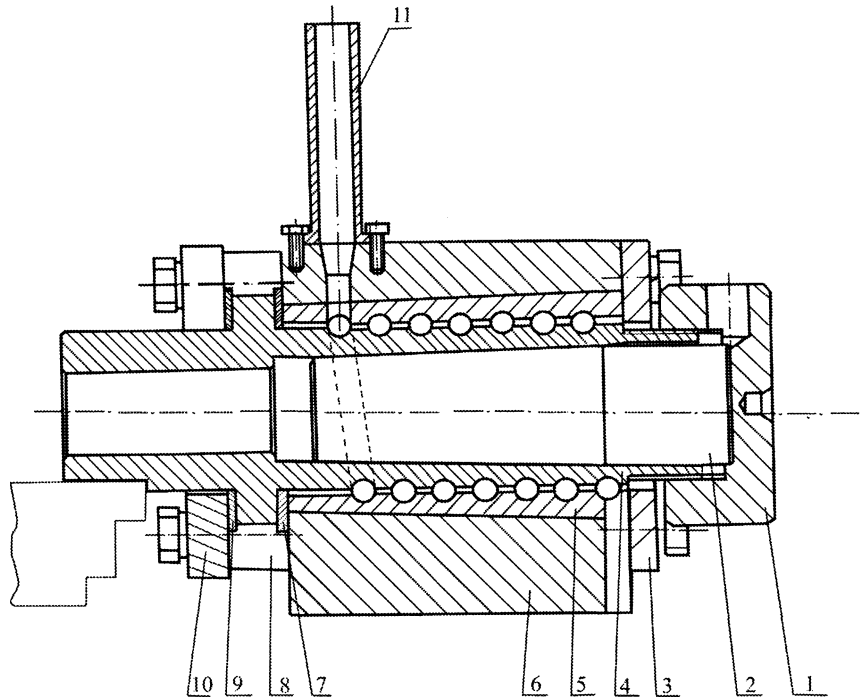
Инструмент для обкатки шариков: 1 – гайка прижимная; 2 – оправка; 3 – крышка; 4 – шнек; 5 – вставка; 6 – корпус; 7, 9 – шайба; 8 – втулка; 10 – крышка; 11 – накопитель шариков
